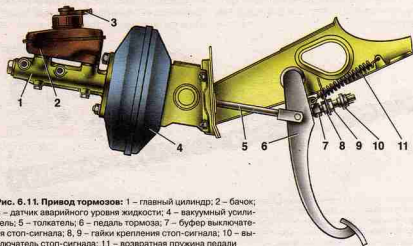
Привод тормозов: 1 – главный цилиндр; 2 – бачок; 3 – датчик аварийного уровня жидкости; 4 – вакуумный усилитель; 5 – толкатель; 6 – педаль тормоза; 7 – буфер выключателя стоп-сигнала; 8, 9 – гайки крепления стоп-сигнала; 10 – выключатель стоп-сигнала; 11 – возвратная пружина педали
